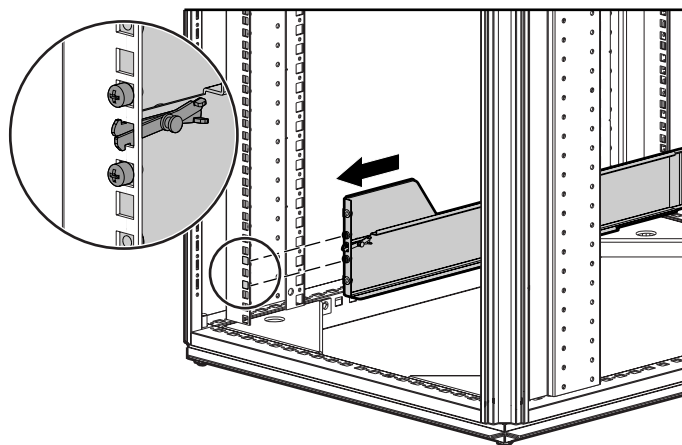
Inserimento della parte anteriore della guida sinistra nel rack
